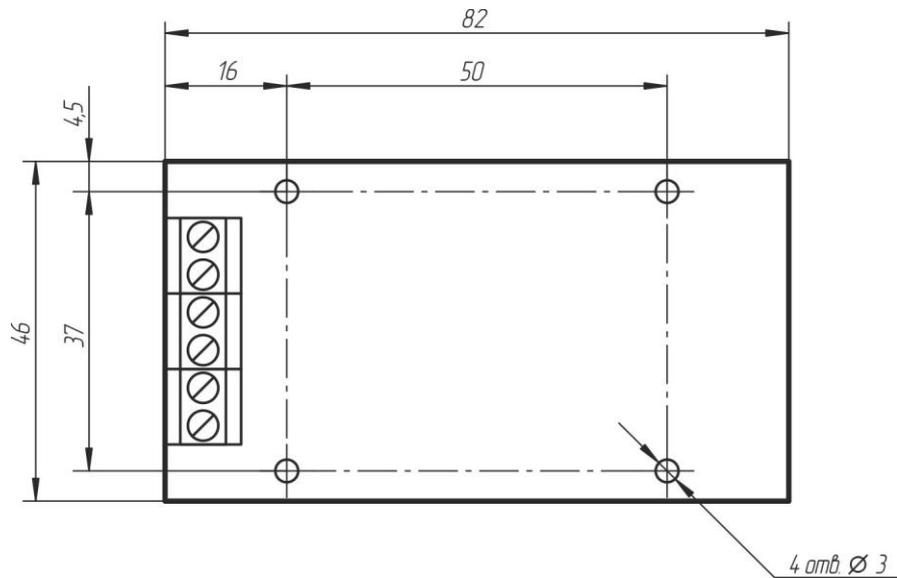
Габаритные и установочные размеры модуля защиты
